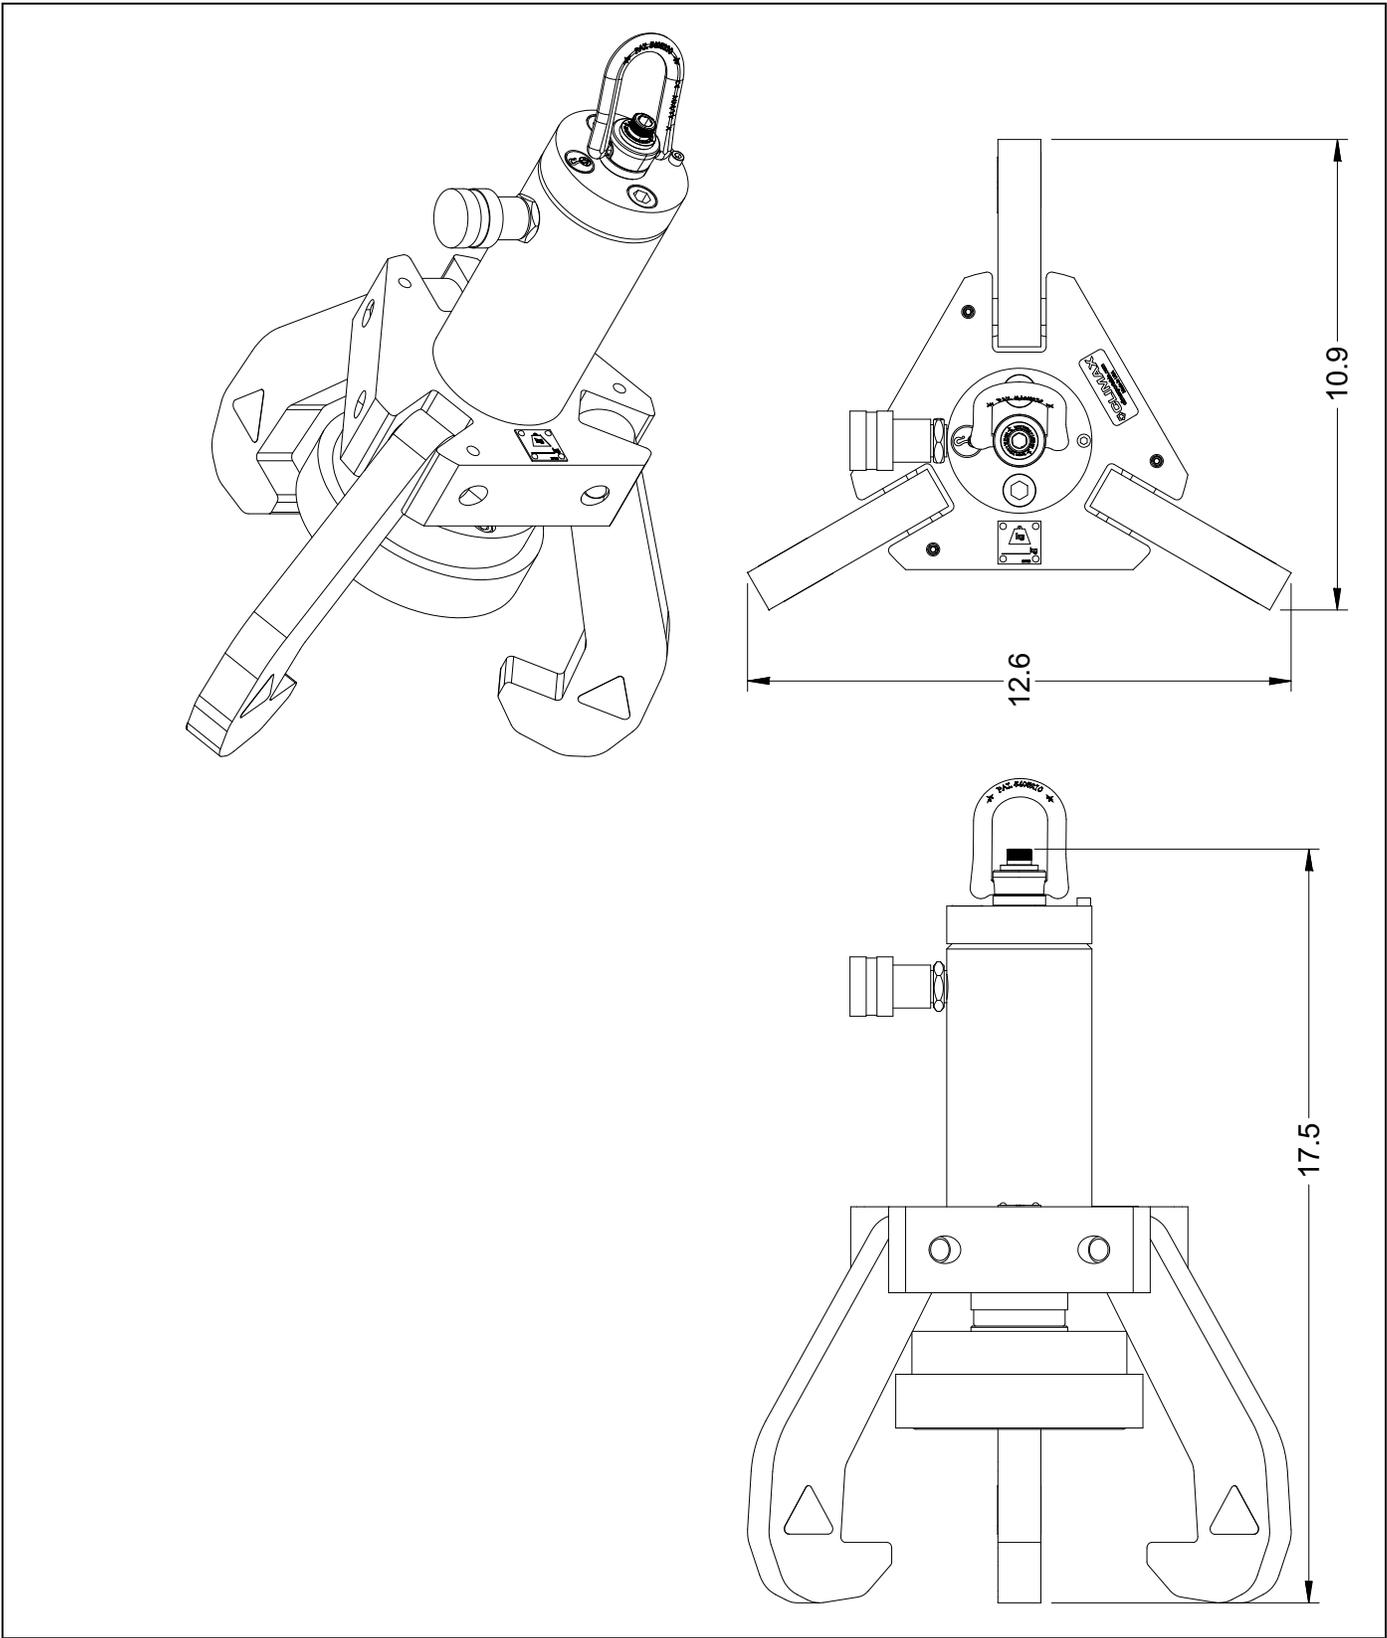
DIMENSIONS DE LA HFS-4
